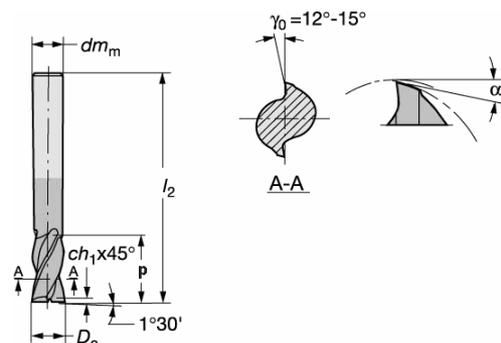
Fresa utilizada (Ref.ª R216.32-06030 AC10A H10F, Sandvik<sup>®</sup>)
